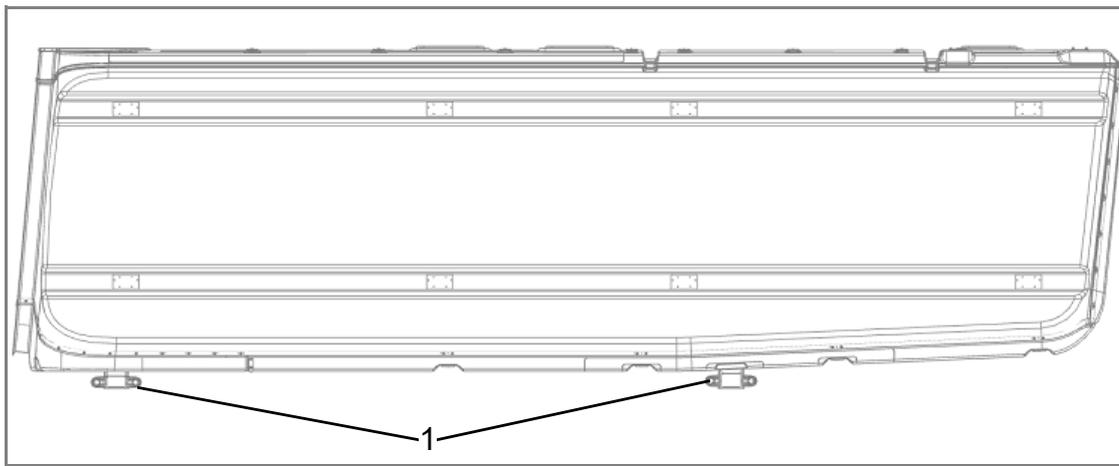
Maschinenhaus, Ansicht seitlich mit Transportfüßen (1)
